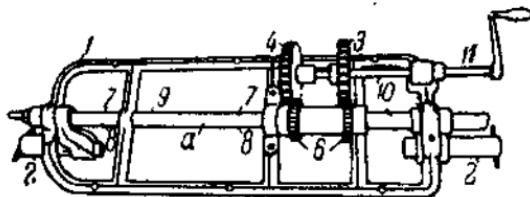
Прибор „Хемпи-Купер С-2“ для расточки коренных подшипников.
